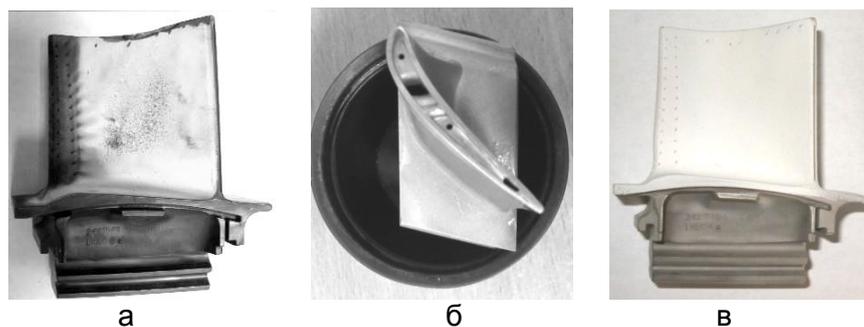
Внешний вид рабочих лопаток 1-ой ступени газовой турбины SGT-800:
